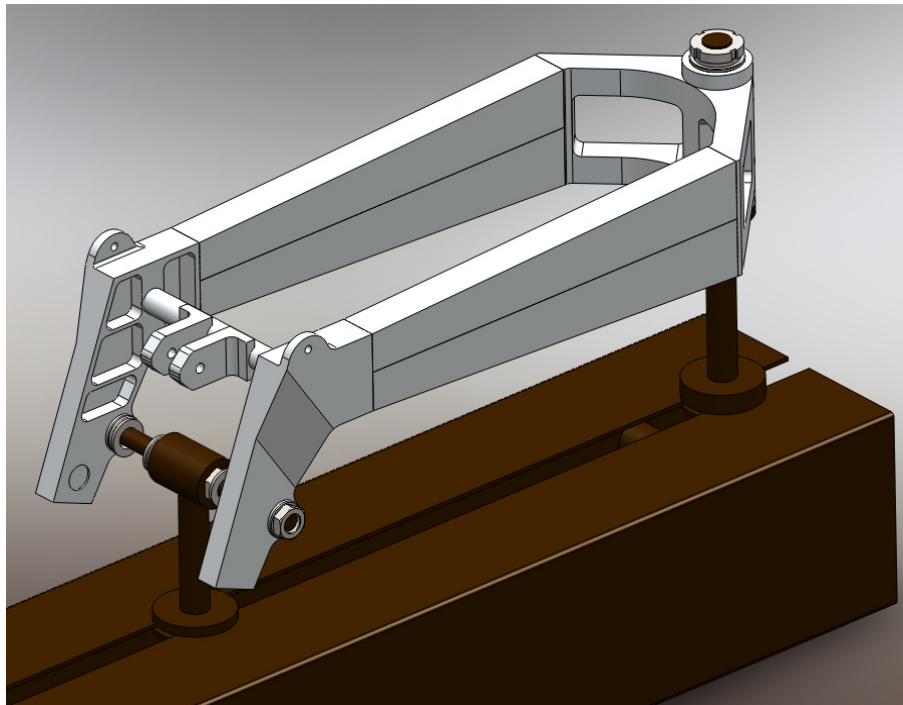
Soldadura de las pletinas con las vigas
